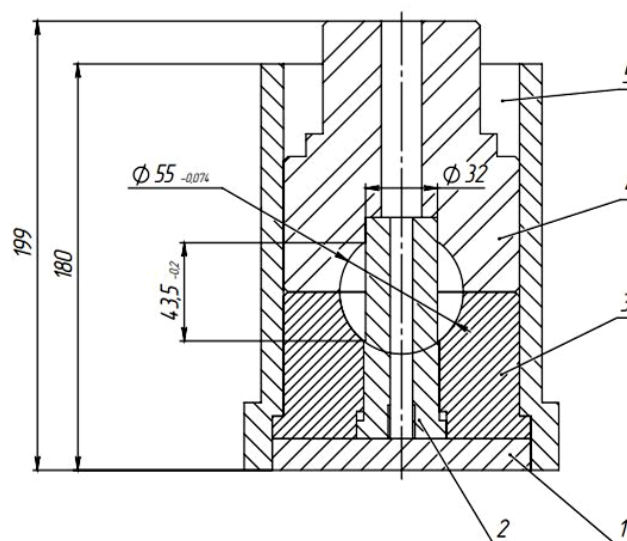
Лабораторная штамповая оснастка: 1 – плита; 2 – оправка; 3 – нижняя полуматрица; 4 – верхняя полуматрица; 5 – корпус
